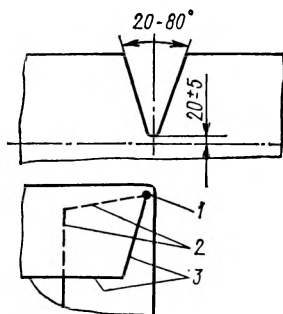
Выкройка и сварка швов на трехгранных углах пластиковой футеровки:
